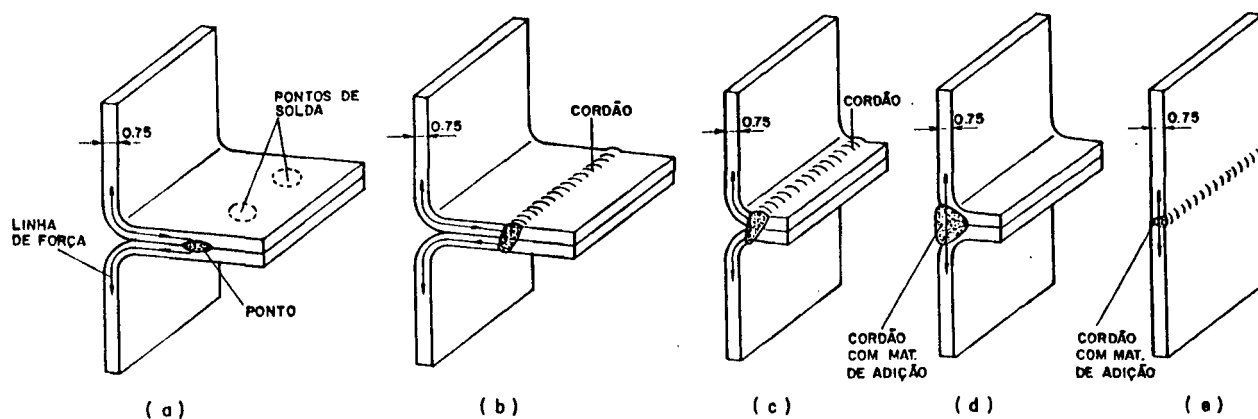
Evolução na soldagem automática de chapas finas: (a) soldagem intensivamente praticada hoje; (e) caso ideal.
